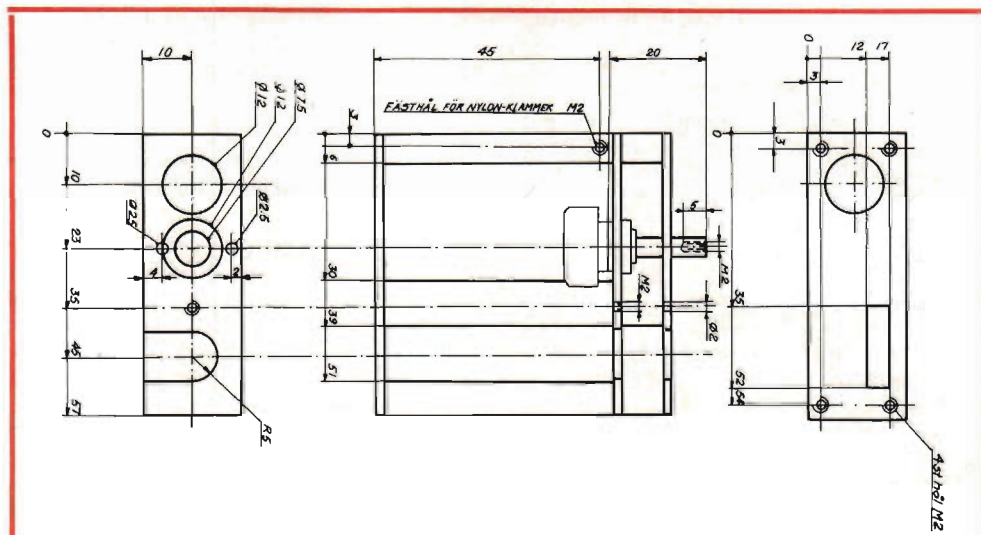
Servomekanismens dimensioner. Alla mått i mm.
